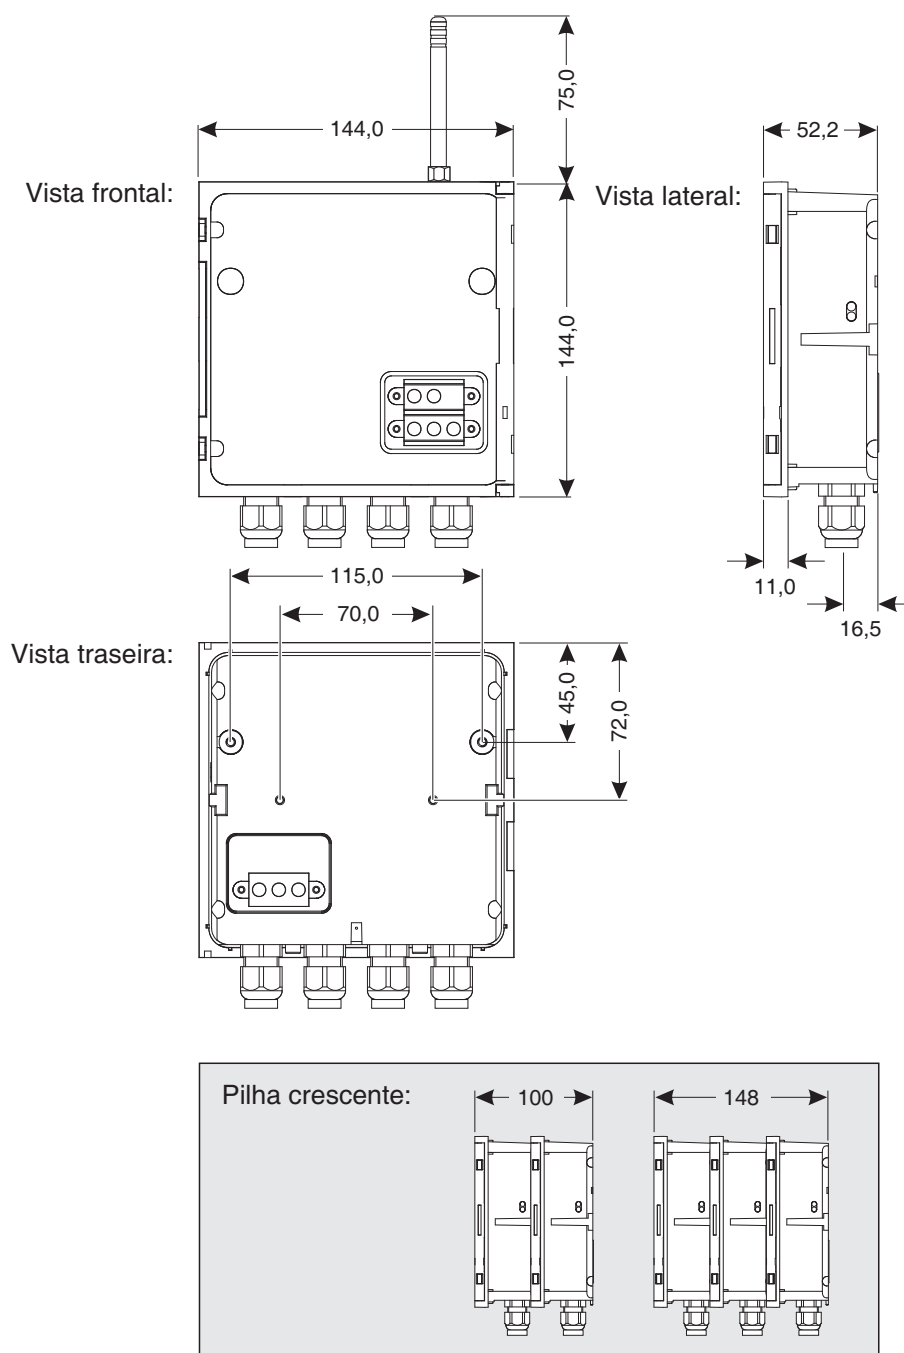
Esboço das dimensões do módulo MIQ^o (dimensões em mm)
